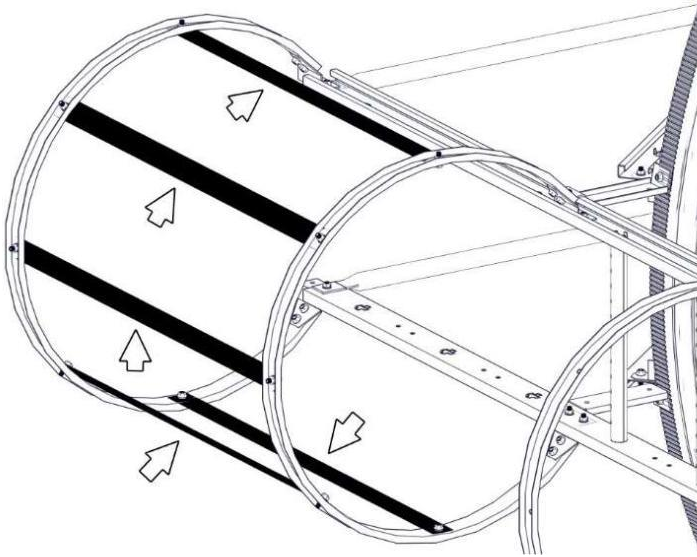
ENSAMBLAJE DE CONJUNTO DE BARRAS DE SOPORTE DE BARANDILLAS
